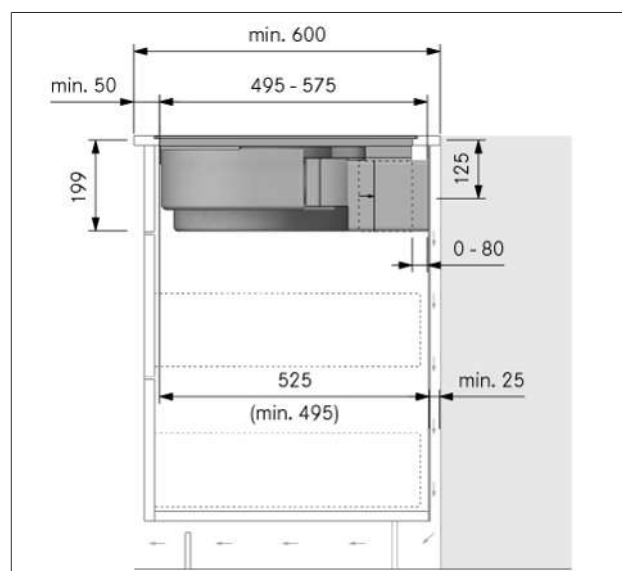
Dimensioni di montaggio con sistema filtrante, variante di montaggio A
